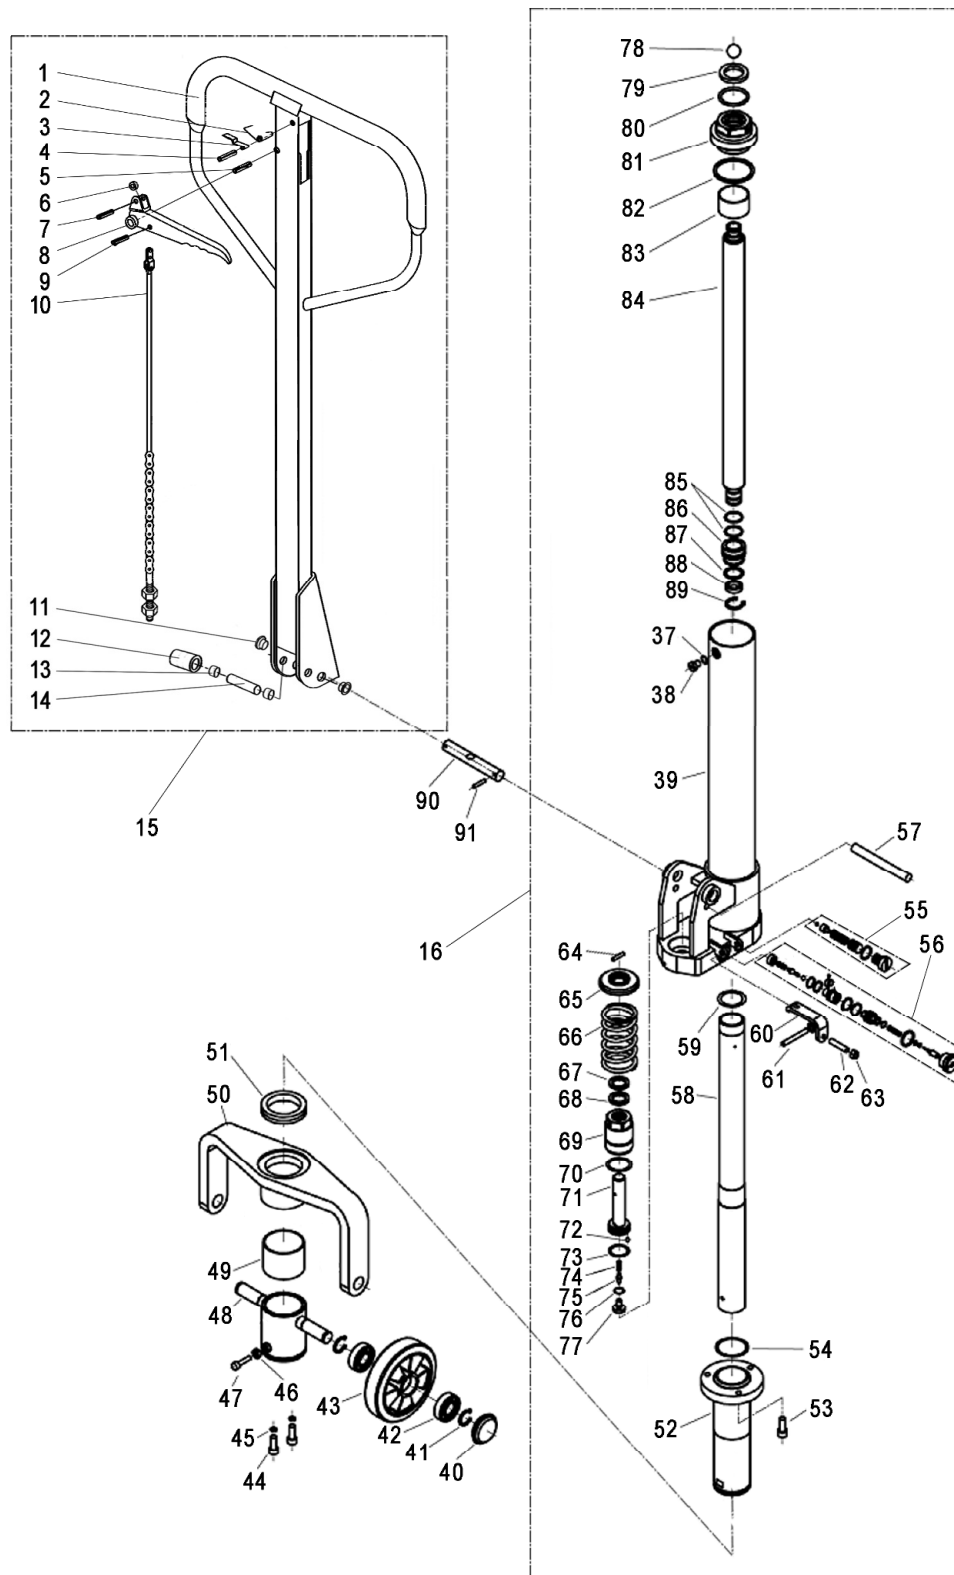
Vista explodida: lança, bomba hidráulica e roda diretriz
